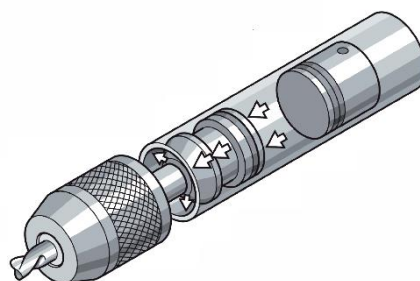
Пневматический ударный механизм перфоратора
